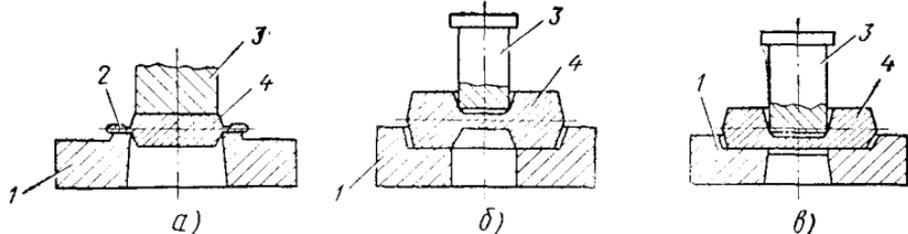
Схемы обрезки (а), прошивки (б) и пробивки (в):
